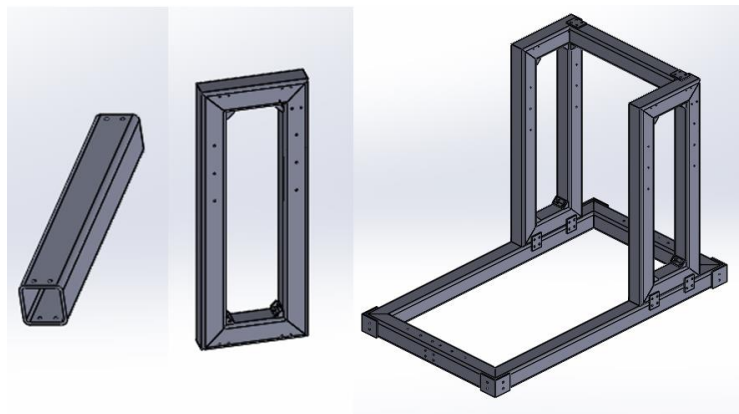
Profilé carré, cadre mécano-soudé et châssis.
